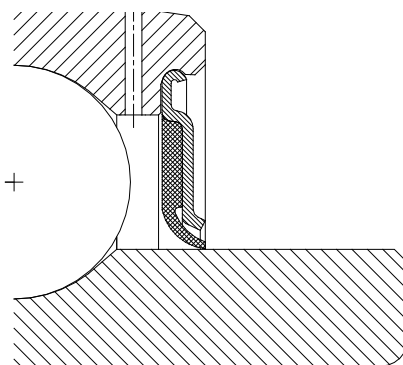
уплотнение корпусных подшипников NKE типа P.
